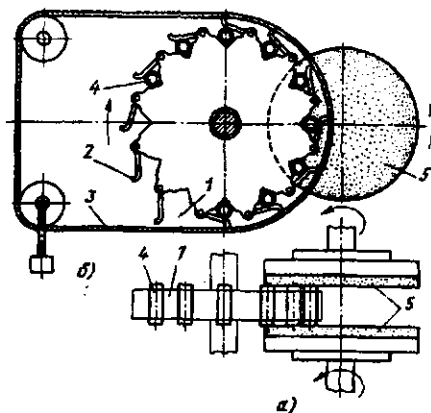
Схема шлифования торцов поршневого пальца: а – одновременное шлифование двух торцов; б – подвод и закрепление обрабатываемой детали
